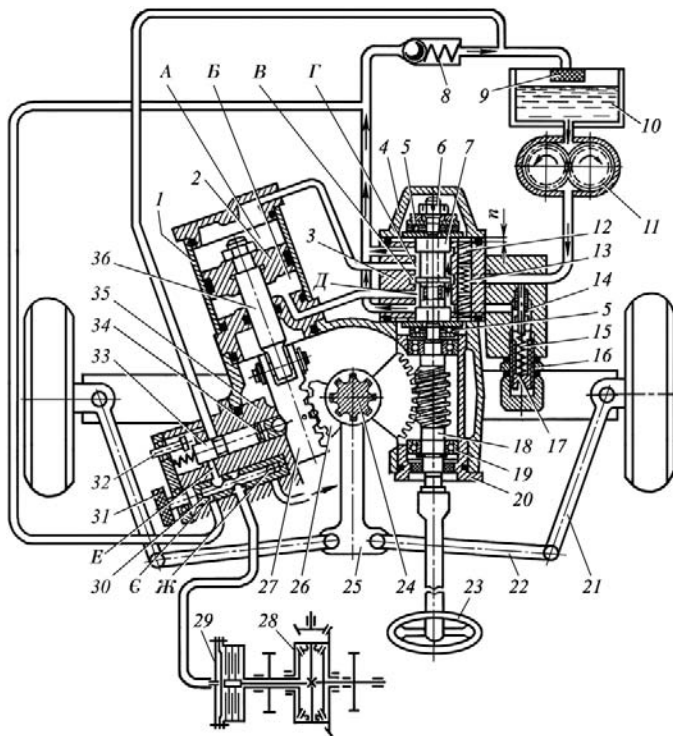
Схема рулевого управления с гидроусилителем трактора МТЗ-80: 1 — силовой цилиндр; 2 — поршень; 3 — корпус распределителя; 4 — крышка; 5 — упорный подшипник; 6 — гайка; 7, 33 — золотники; 8 — редукционный клапан; 9 — фильтр; 10 — масляный бак; 11 — шестеренчатый насос; 12 — ползун; 13 — центрирующая пружина; 14 — предохранительный клапан; 15 — пружина; 16 — контргайка; 17 — регулировочный винт; 18 — червяк; 19 — шариковый подшипник; 20 — эксцентричная втулка; 21 — поворотный рычаг; 22 — рулевая тяга; 23 — рулевое колесо; 24 — поворотный вал; 25 — сошка; 26 — сектор; 27 — рейка; 28 — дифференциал; 29 — диафрагма блокировки дифференциала; 30 — кран; 31 — маховик; 32 — шуп; 34 — толкатель; 35 — упор; 36 — шток силового цилиндра; А, Б — полости силового цилиндра; В — средняя нагнетающая виточка; Г, Д — крайние сливные выточки; Е — сливной канал датчика; Ж — дроссельное отверстие.
